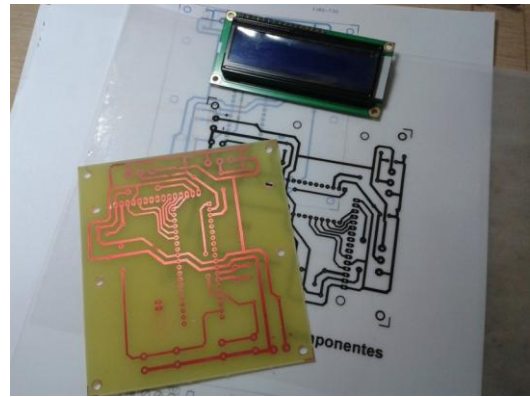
DISEÑO E IMPRESIÓN DEL PCB.
